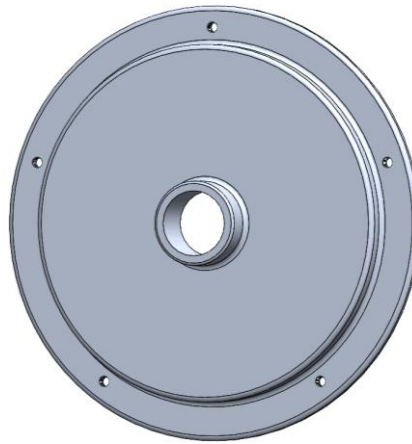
Modelo geométrico CAD 3D de la tapa frontal de la carcasa: vista frontal.
